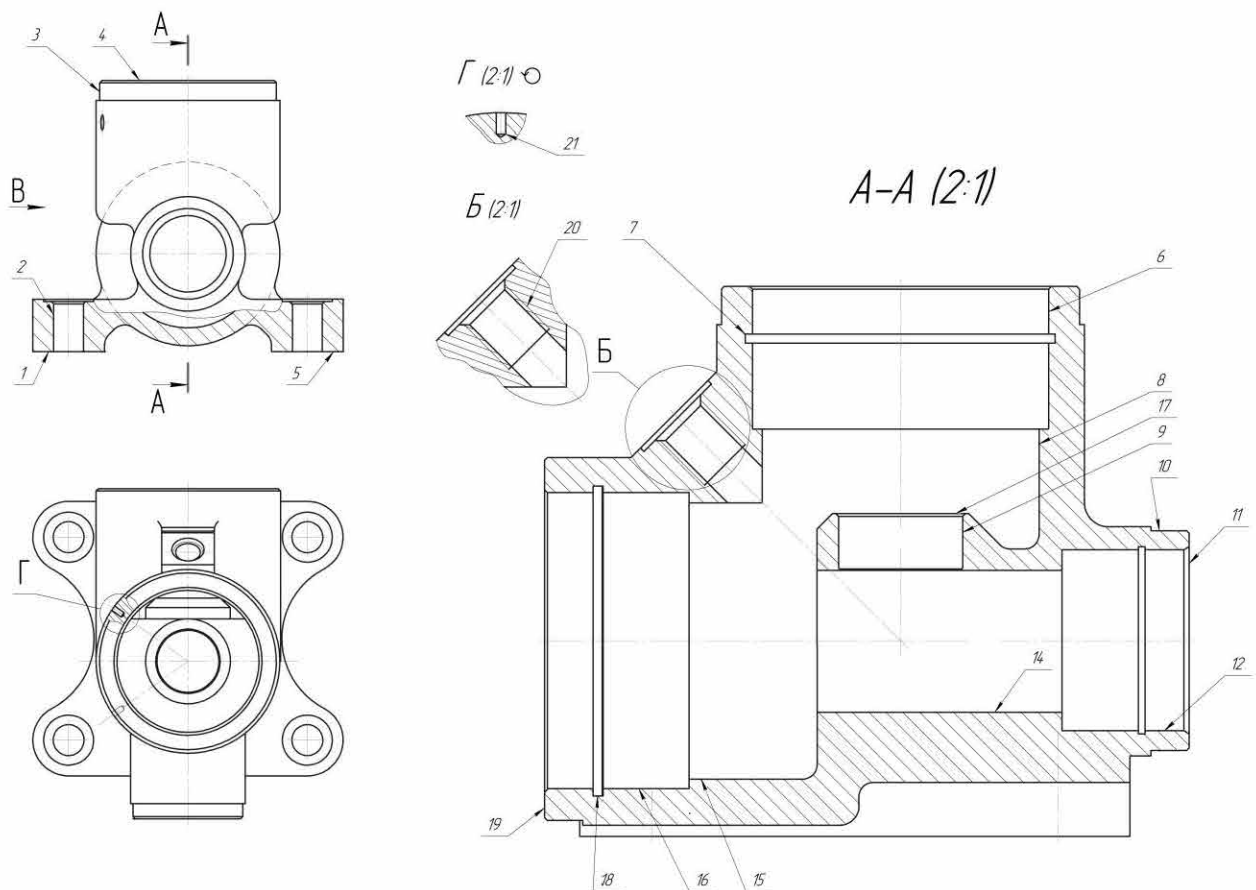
Ескіз деталі корпус УЯИШ.731347.006
